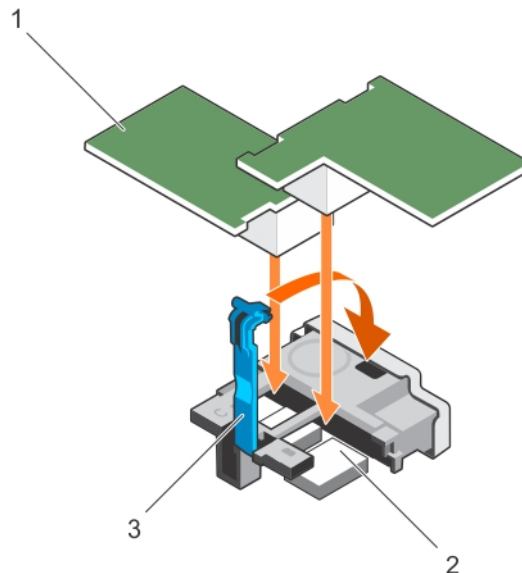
Installieren einer PCIe-Mezzaninkarte
